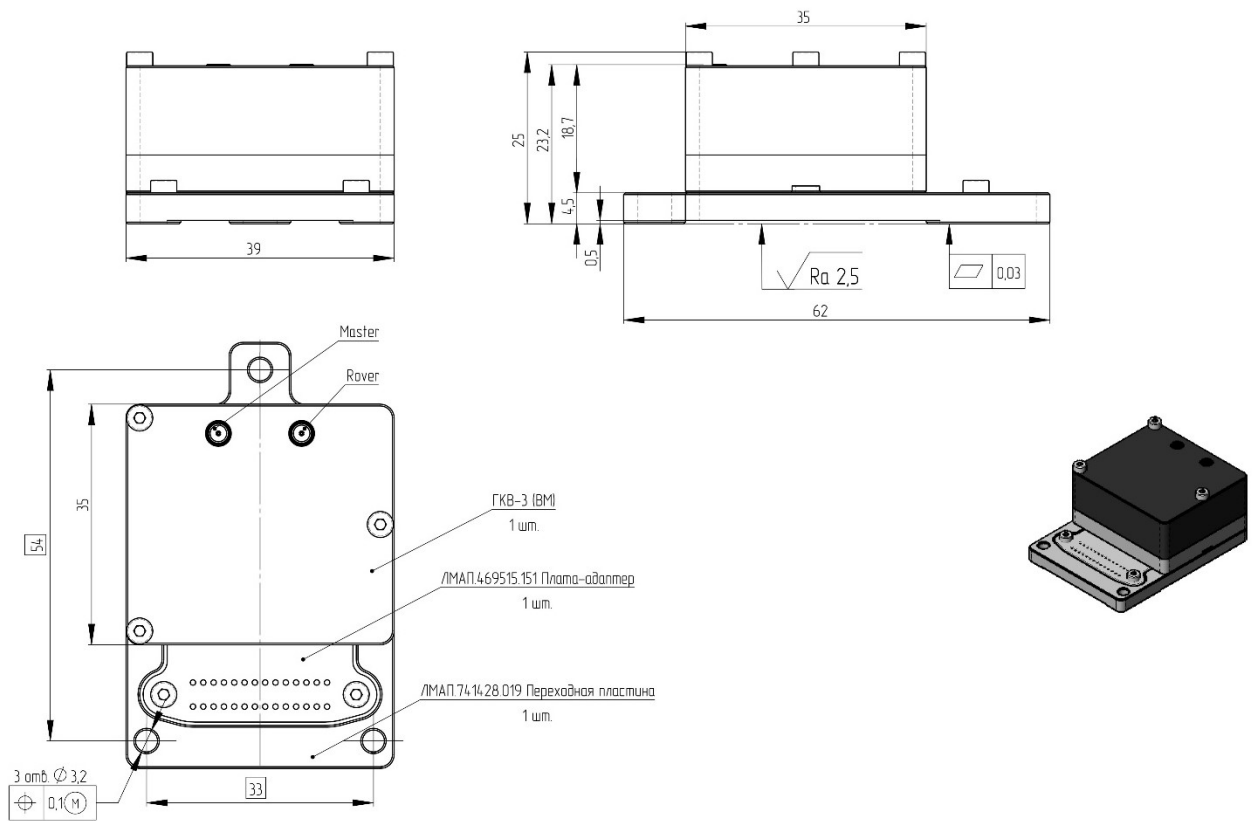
Внешний вид переходной дюралевой пластины с печатной платой
